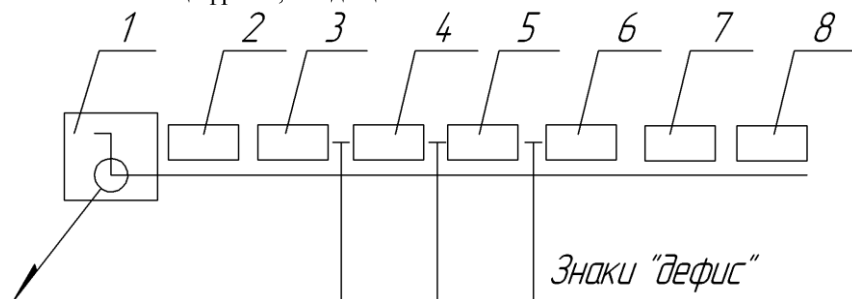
Структура обозначения сварного шва по ГОСТ 2.312-72
